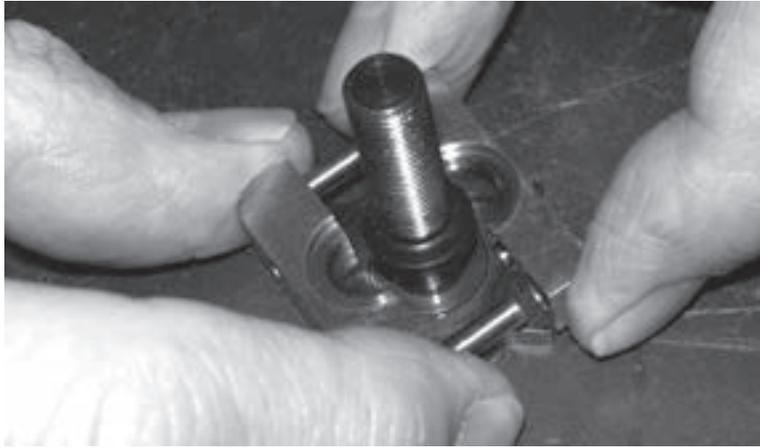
Die Buchsenschrauben sichern die Vorschubbuchse an ihrer Position.
